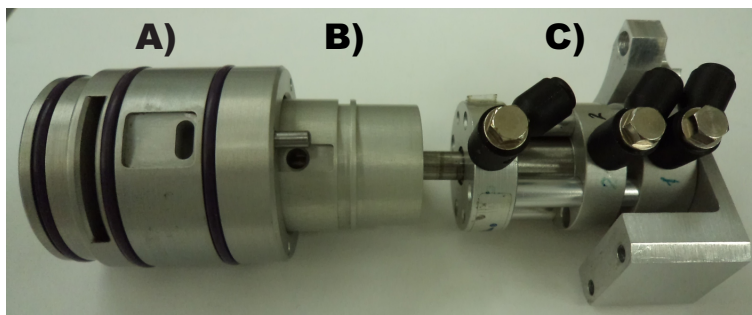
Componentes principales del blanco sólido: A) sujetador, B) inserto, C) cilindro neumático.
